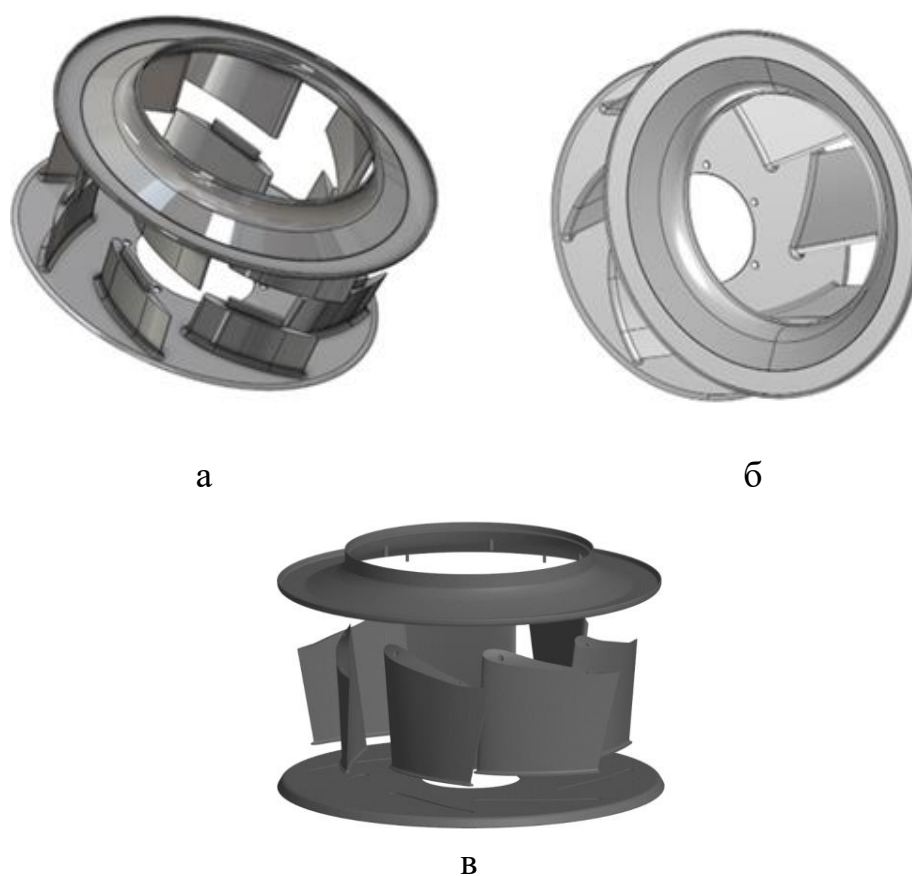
Варианты конструкции рабочего колеса: а – колесо из двух частей; б – цельное колеса; в – колесо из восьми частей
